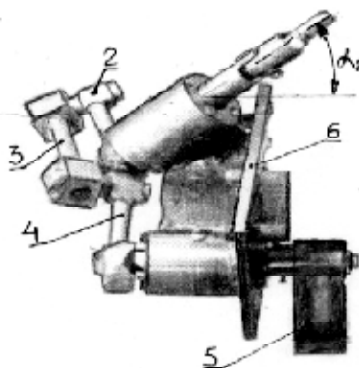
Фото корпуса устройства (иллюстрация авторов)
